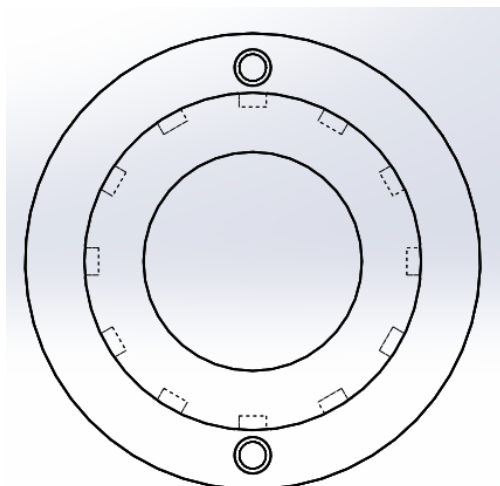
Vista en planta útil rotor (Font: SolidWorks)[14]
